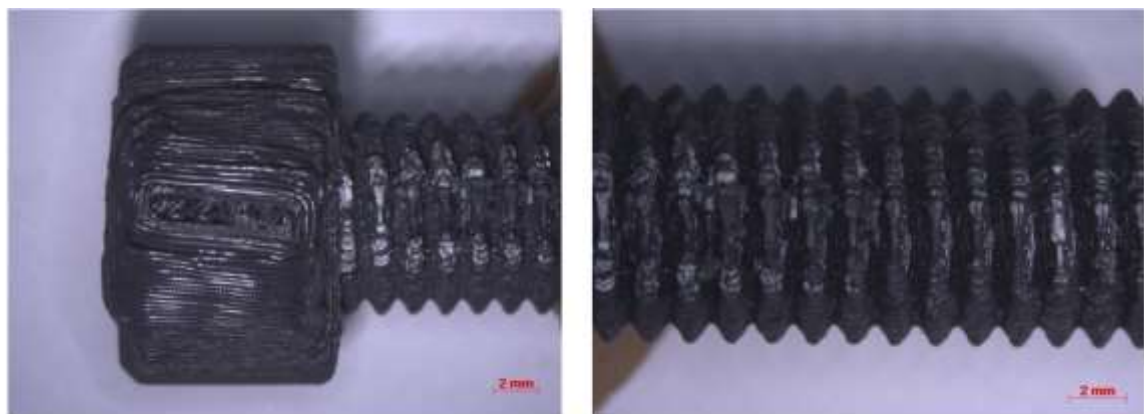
Vista frontal da cabeça (à esquerda) e rosca (à direita) do parafuso impresso com a orientação horizontal.
